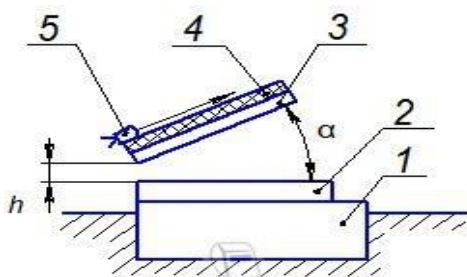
Схема процесу зварювання вибухом: 1 – опорний фундамент; 2, 3 – зварювані деталі; 4 – шар вибухової речовини; 5 – детонатор; h – зазор між деталями; α – кут установлення деталей
